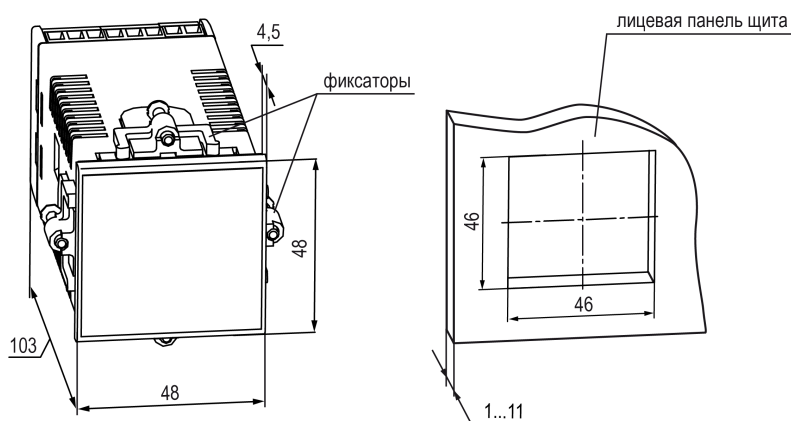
Габаритные размеры корпуса Щ5 и монтажного отверстия в щите
